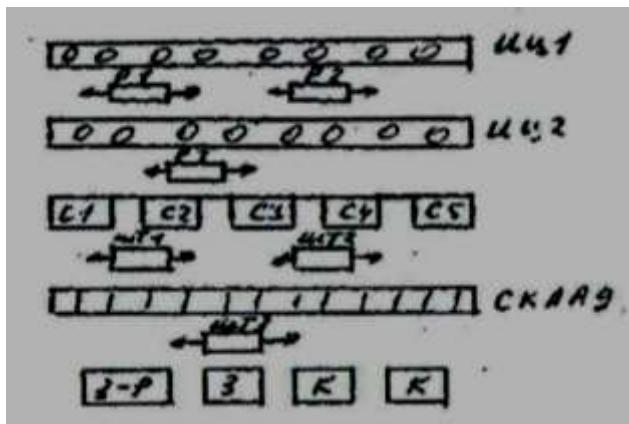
Зразкова схема ГВС з інструментальним складом для заготовок і деталей
